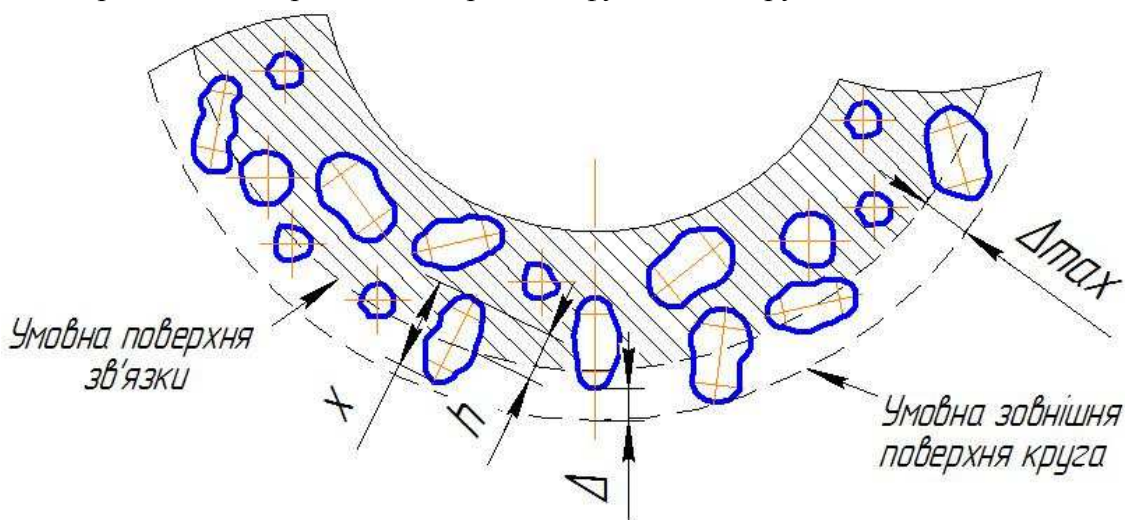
Схематичне зображення робочої поверхні шліфувального круга:
